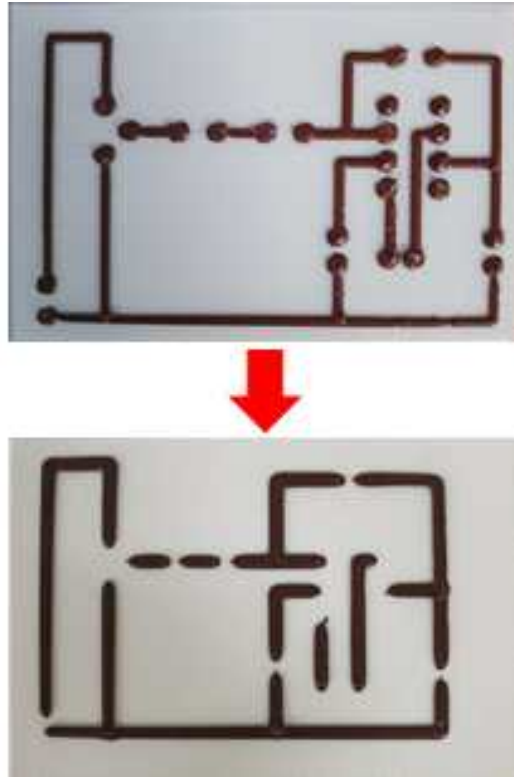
Laser 경화에 의한 Cu 배선의 Width 증가 및 Pad 제거 배선 공정
